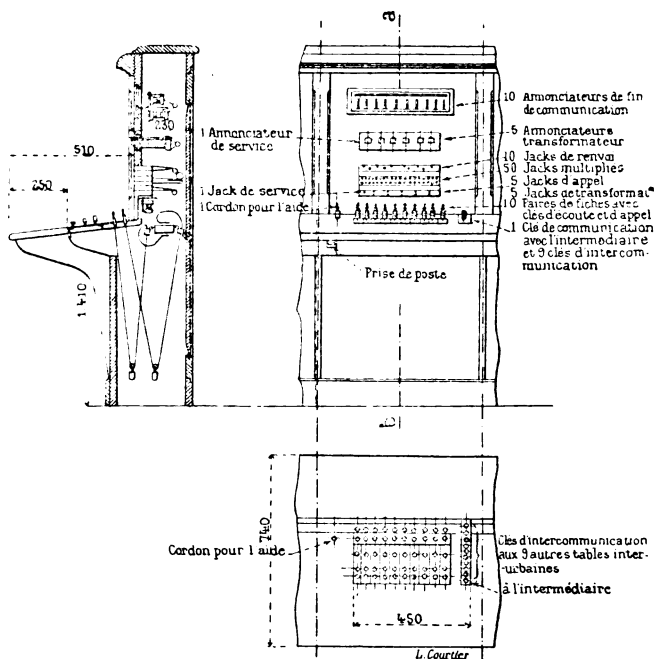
Élévation, plan et coupe d'une table interurbaine.
